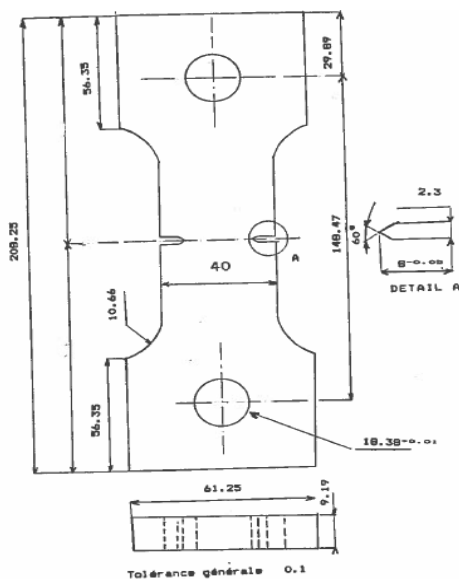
Dimensions de l'éprouvette en (mm).
